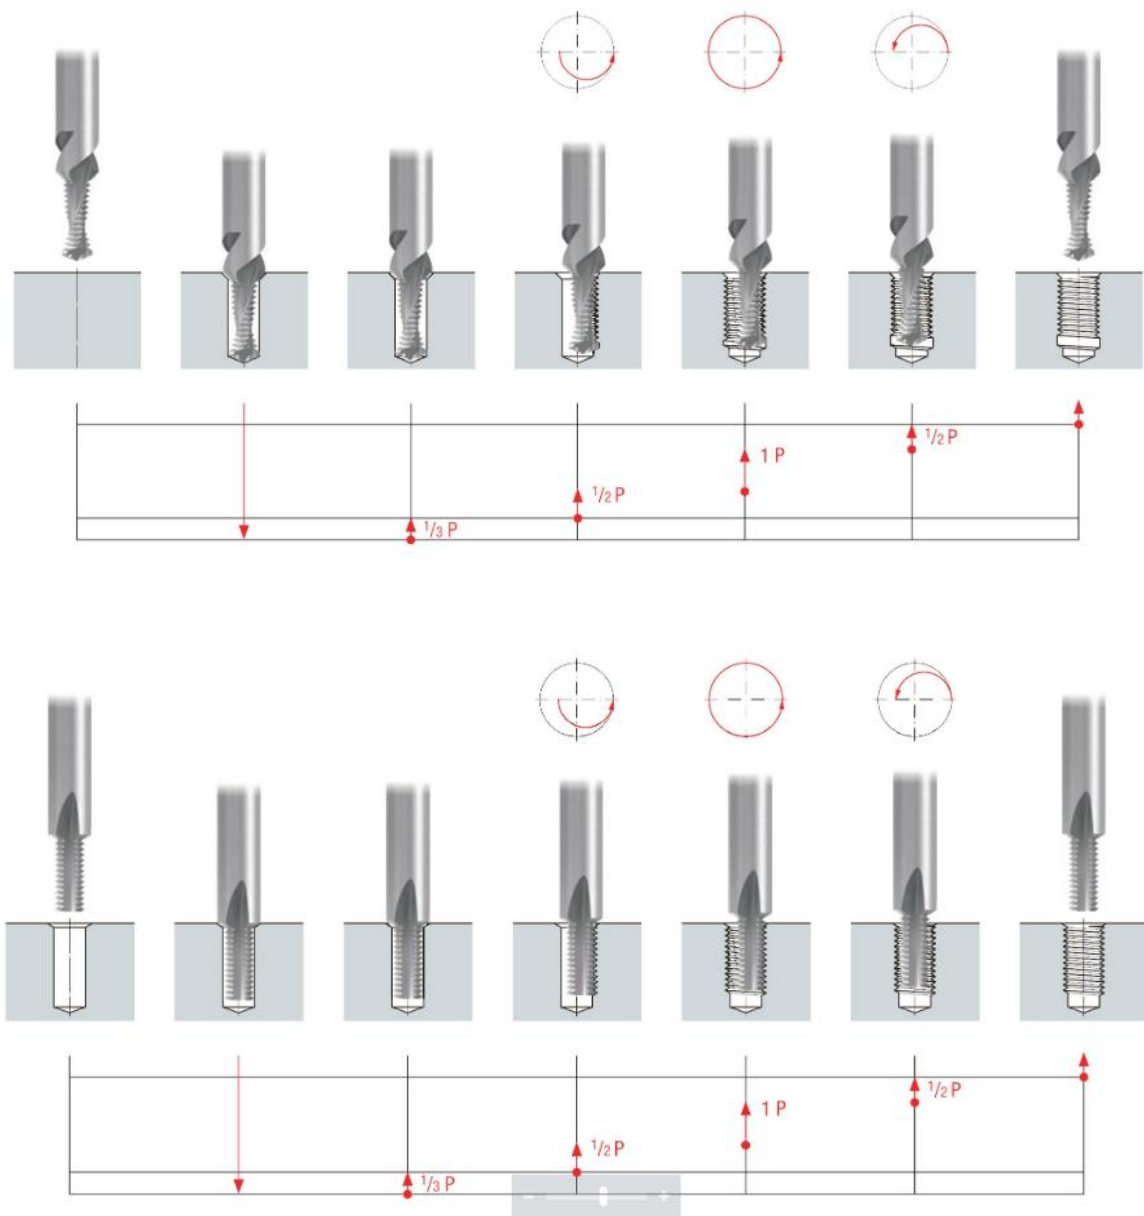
Схеми врізання різьбової фрези у заготовку [22]
